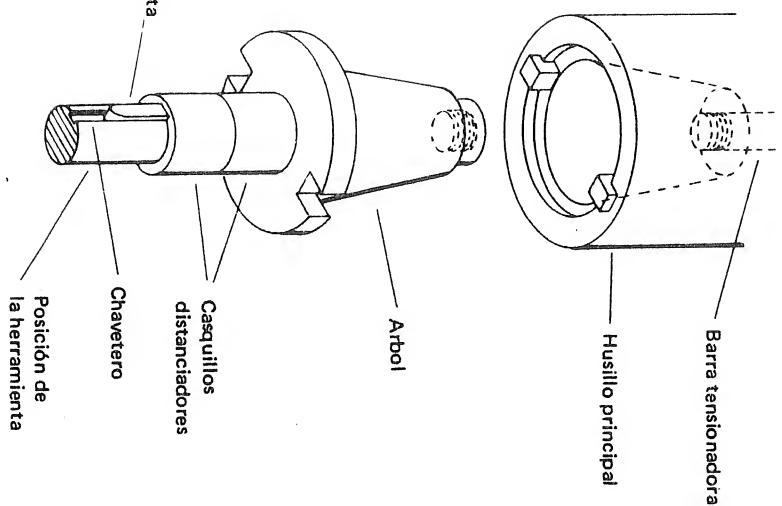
Sujeción de la herramienta en el fresado horizontal.
